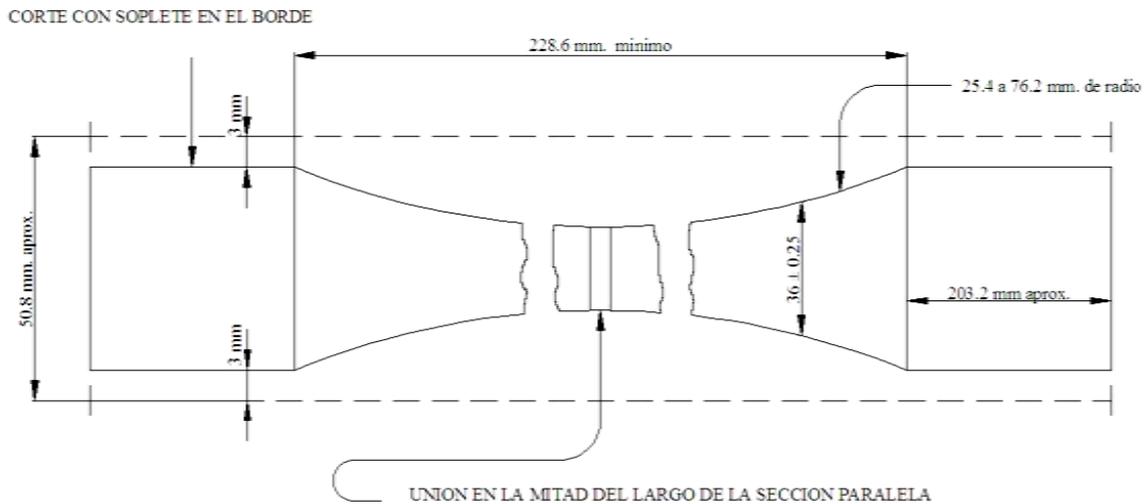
Probeta para prueba a tensión de soldadura
